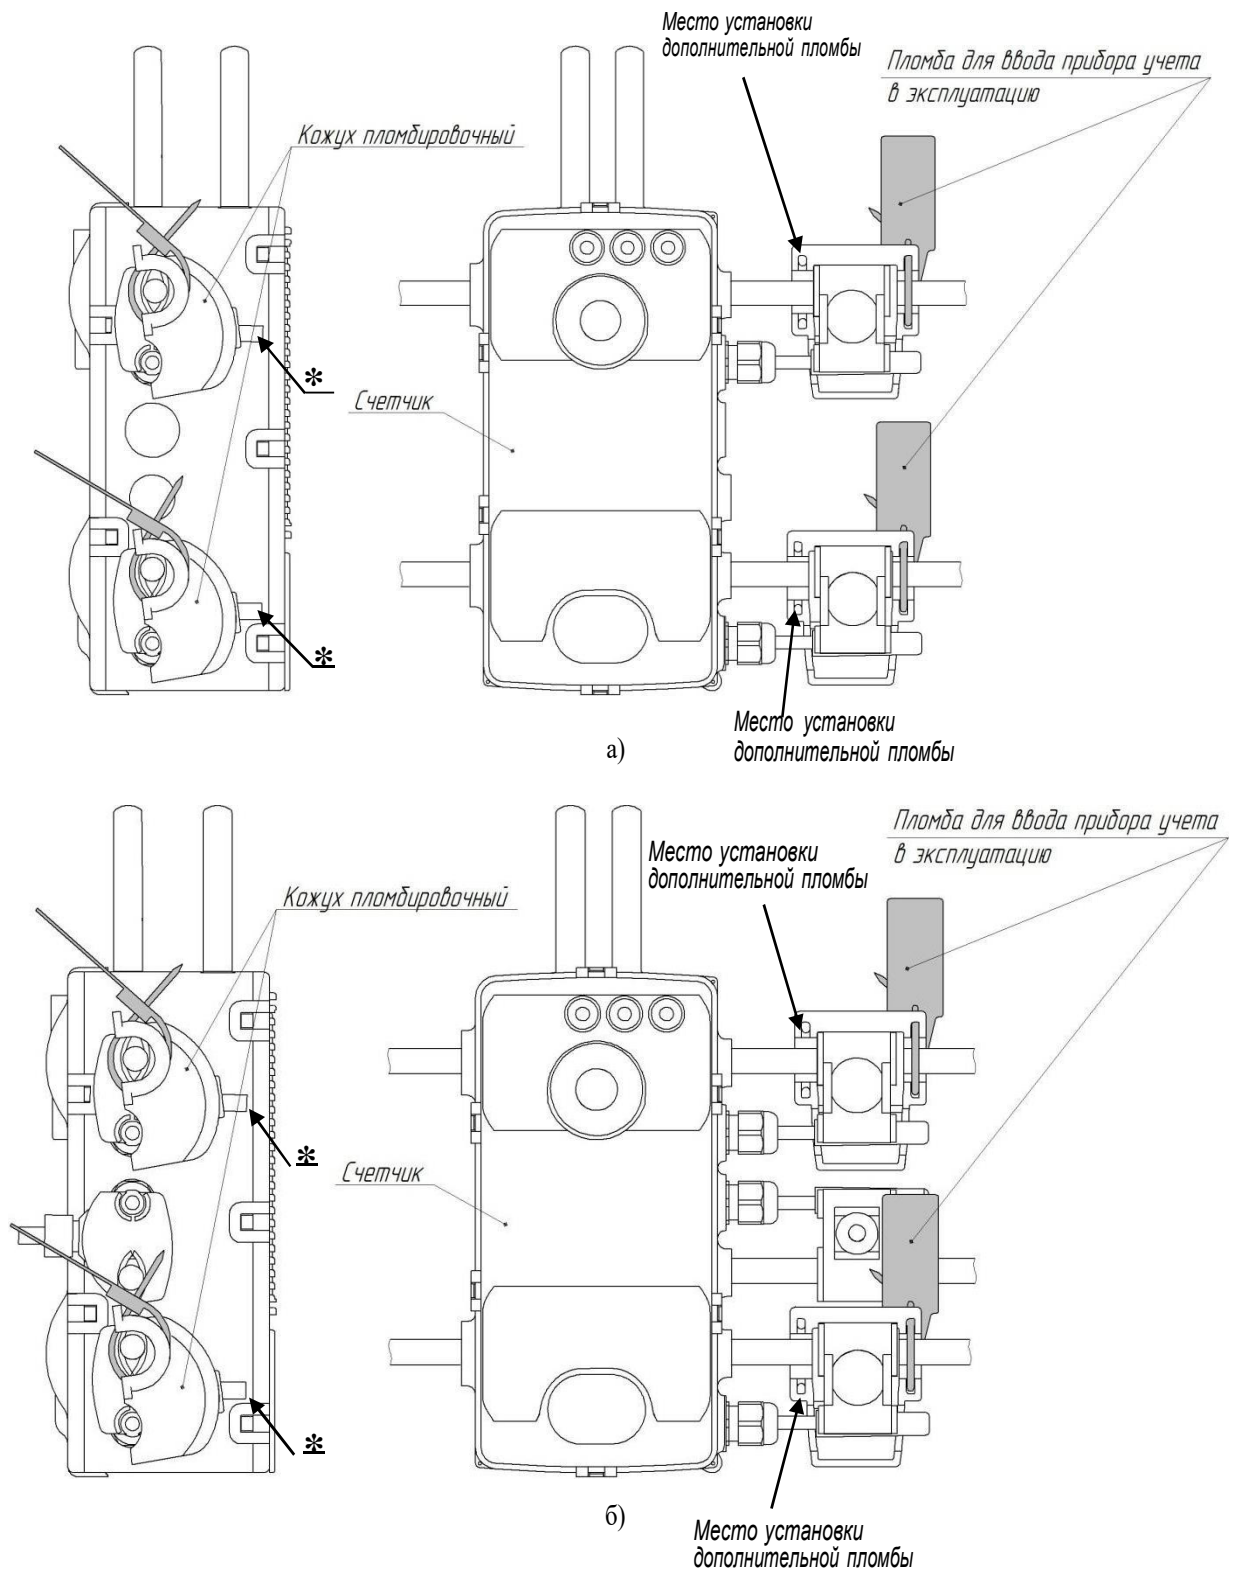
Установка кожуха пломбировочного на счетчики в корпусе Тип IV
